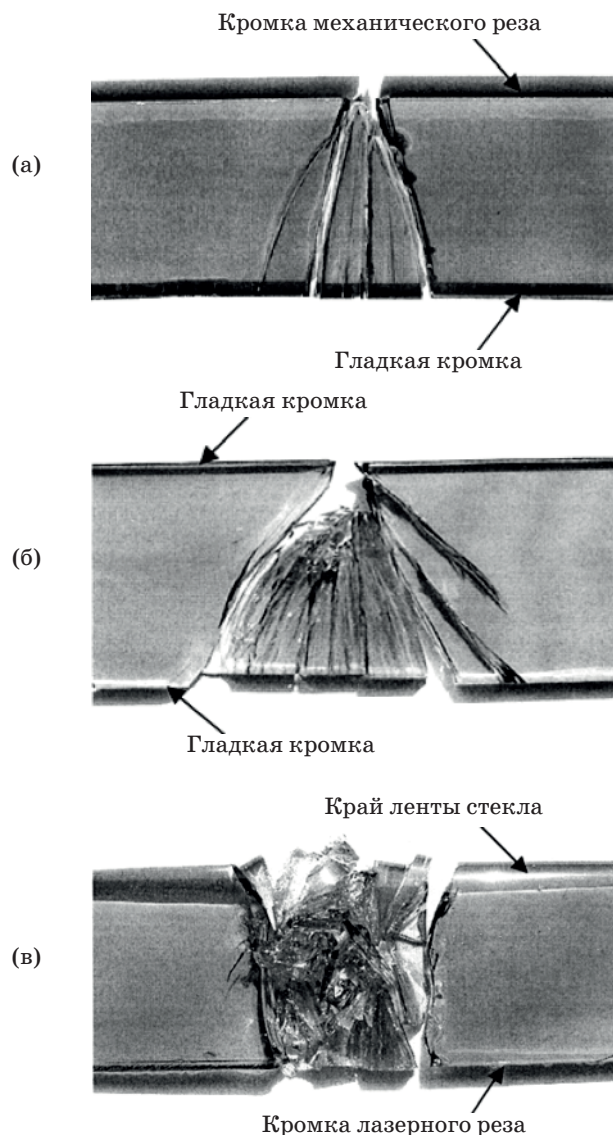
Характер разрушения образцов стекла после различных видов обработки кромок при испытании на поперечный изгиб. а – образец с кромкой механического реза, б – образец с гладкими кромками, в – образец с кромкой лазерного реза.
